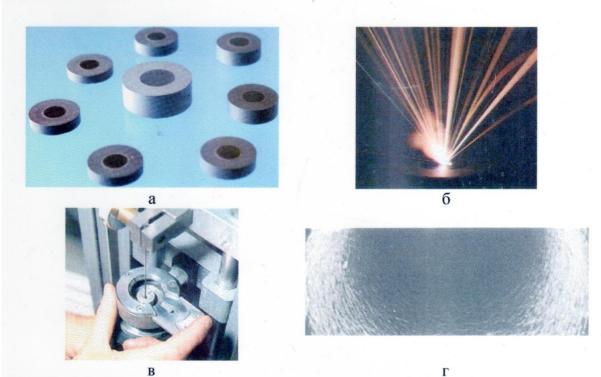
Заготовки для изготовления фильер (a), лазерное прожигание канала в фильере (б), колибровка канала фильеры (в), фнешний вид поверхности канала фильеры (г).
